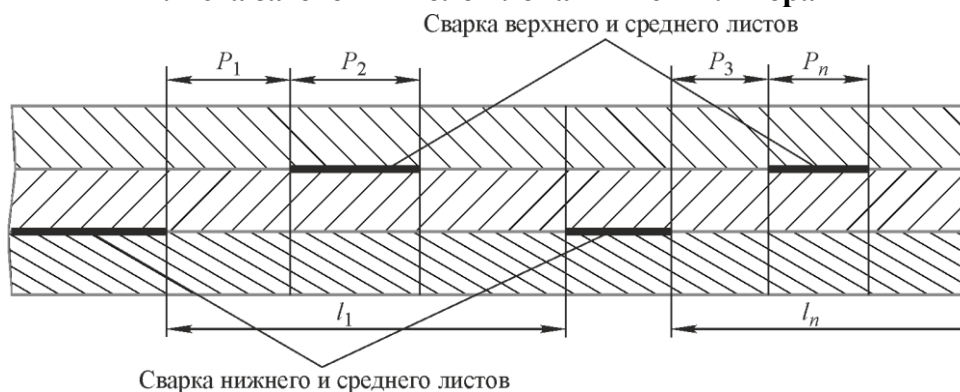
Схема параметризации на фрагменте сечения заготовки полый лопатки для нахождения зон сварки верхнего и среднего листов:
